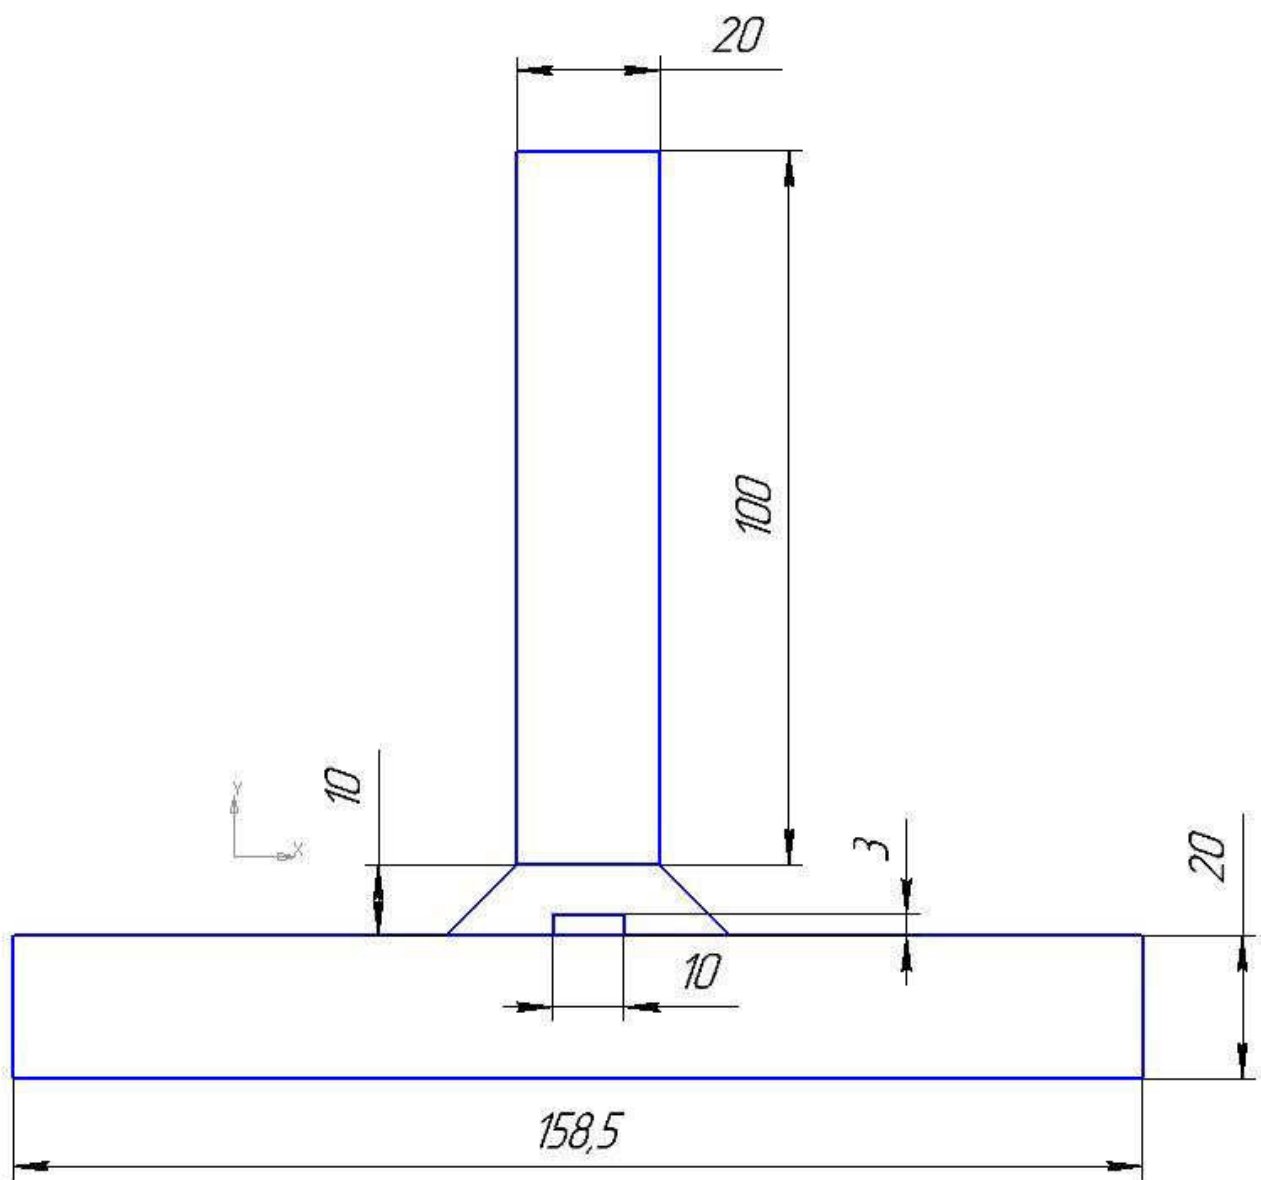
схема сварного таврового соединения с катетом и непроваром
